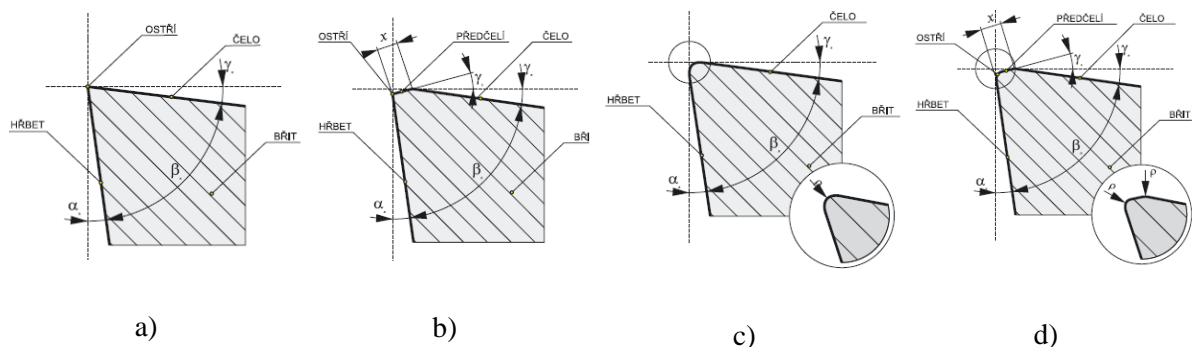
Místo prvního kontaktu obrobku a nástroje s ohledem na základní geometrii [43].
